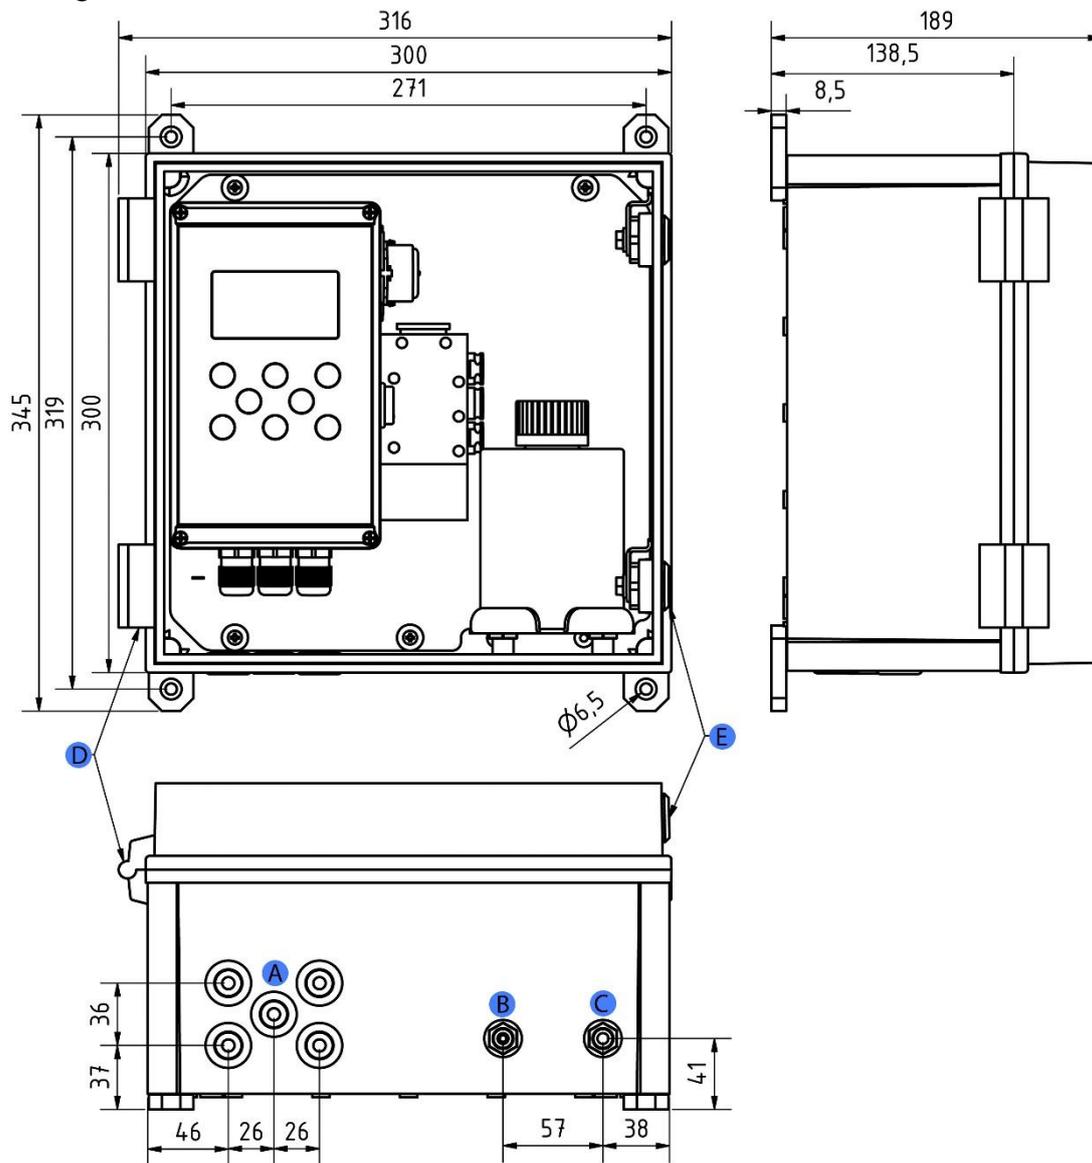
Bohrplan zur Befestigung des Analysegerätes im Gehäuse
